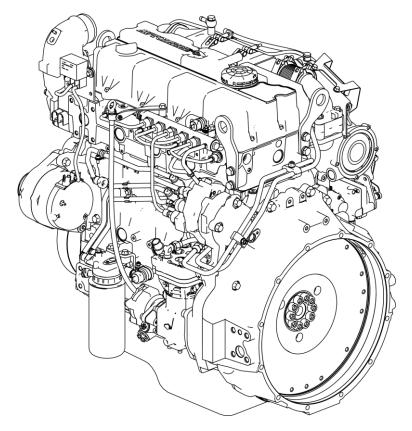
а – Двигатель ЯМЗ-53403-10 (общий вид слева)
